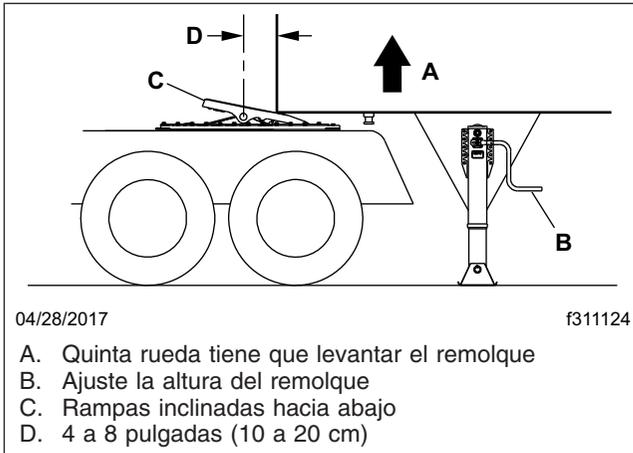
, Punto de conexión del remolque, placa de la quinta rueda estándar
